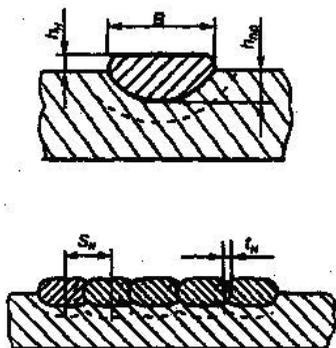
Способы наложения слоёв: B , h , hr – соответственно ширина валика, высота наплавки, глубина проплавления; S_m – шаг наплавки
